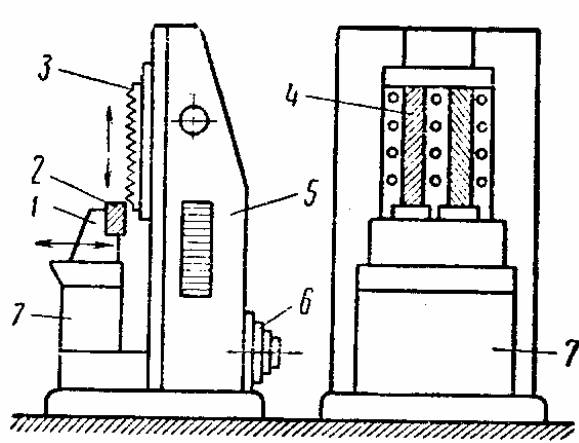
Схема вертикально-протяжного станка для наружного протягивания
